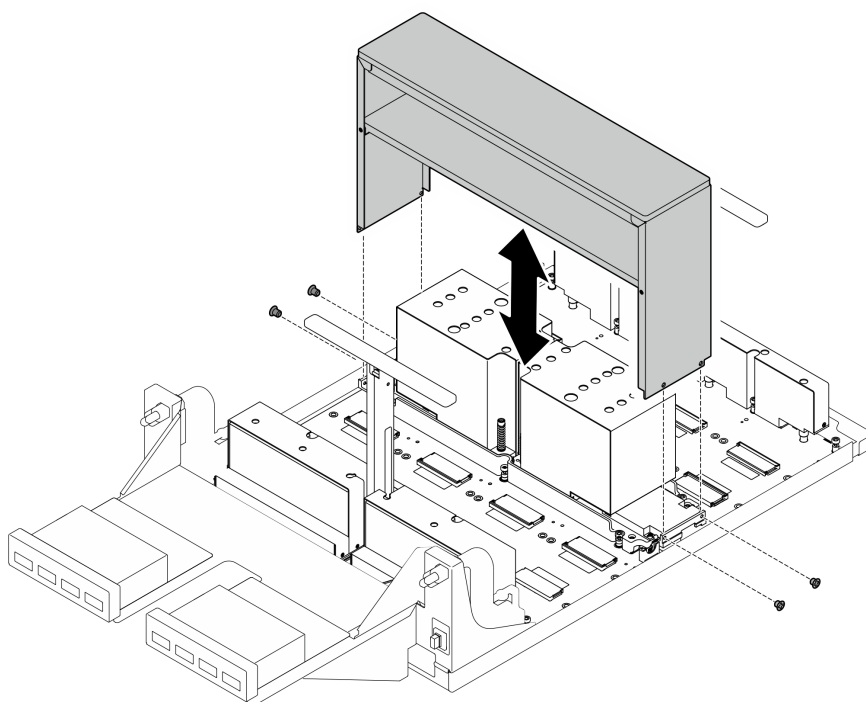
Retrait du cache du dissipateur thermique NVSwitch
